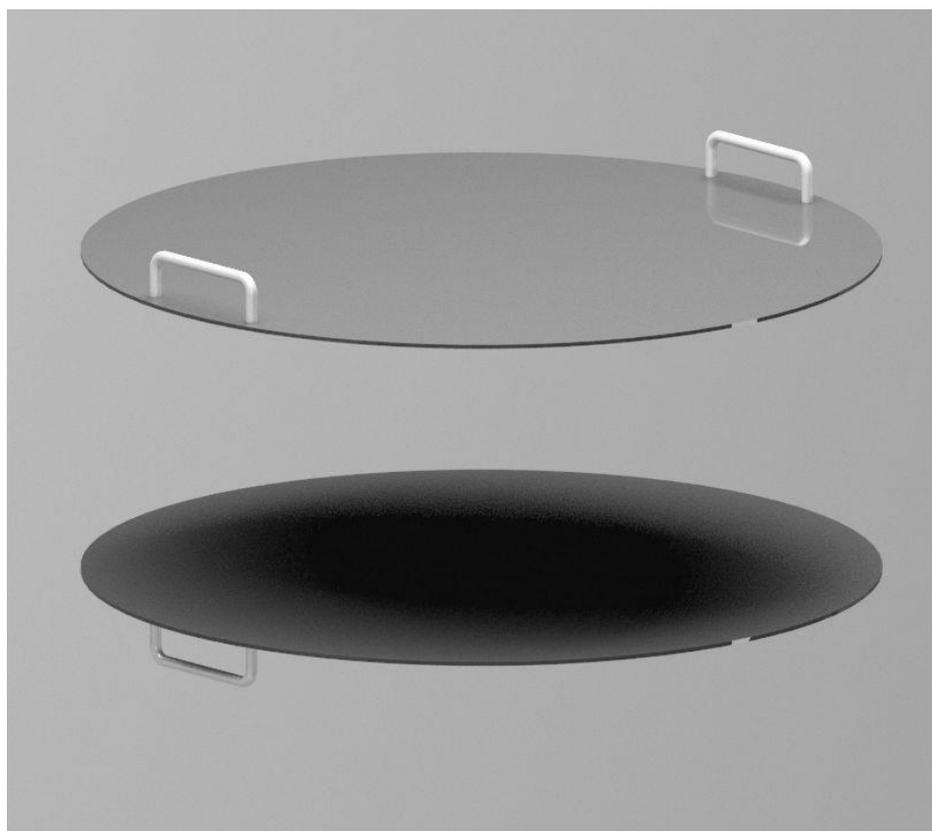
Plancha/quemador removible sin puntos de anclaje.
